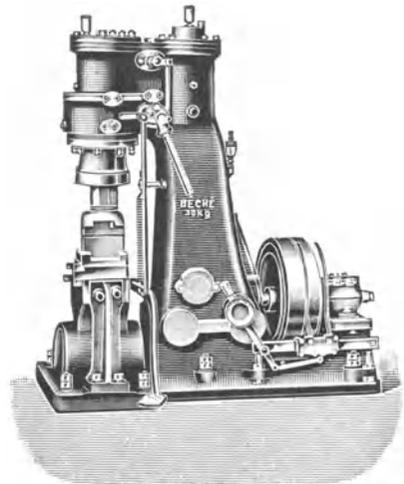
Lufthammer mit schwenkbarer Schabotte.
